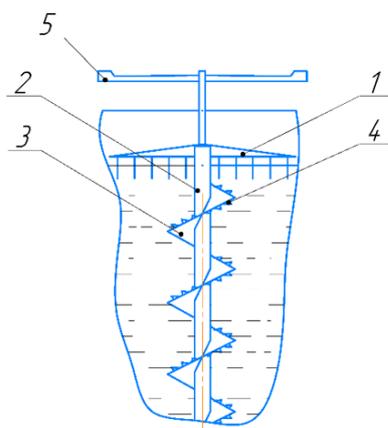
Схема модернизированного биореактора-метантенка ИБГУ-1 [1]: 1 - гребенка; 2 - вал мешалки; 3 - шнек; 4 - режущий сегмент; 5 - рукоятка-крестовина мешалки;
